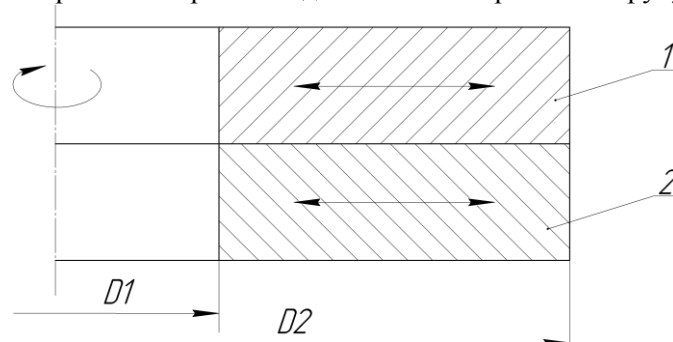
Схема способу правки робочих поверхонь притирів вібровикінчувальних верстатів з обертанням верхнього притира (б).
